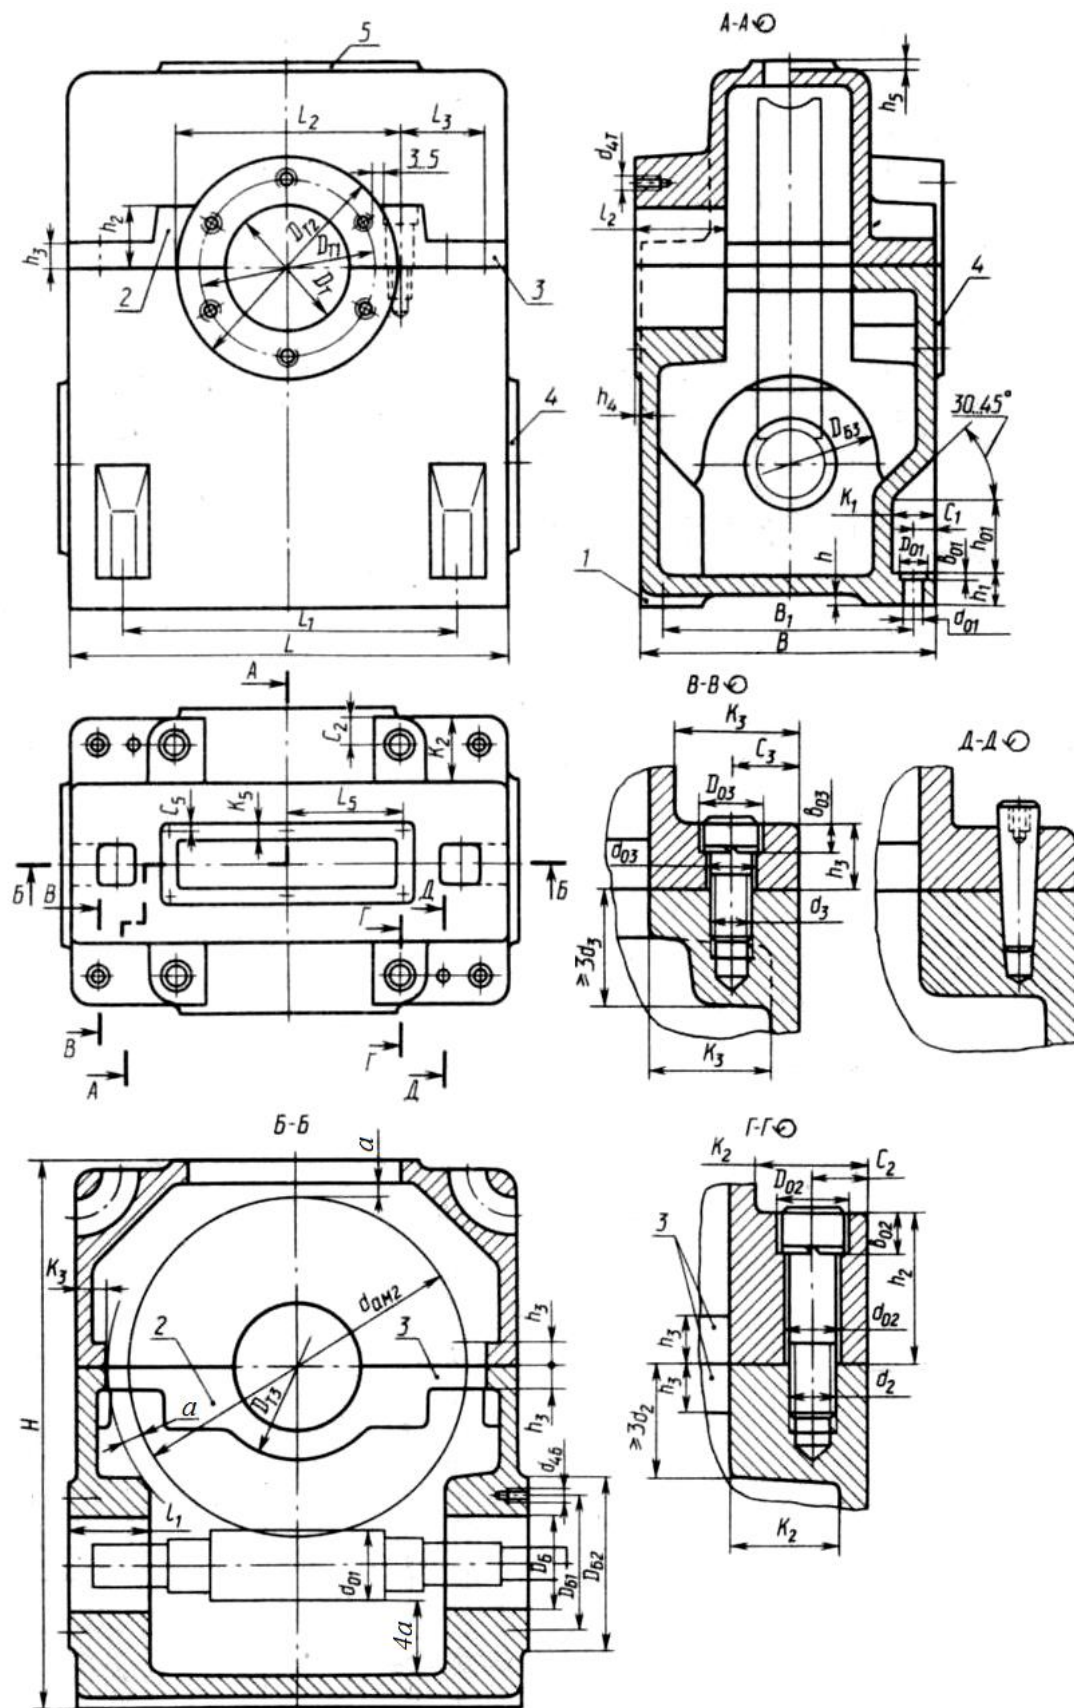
Разборный корпус одноступенчатого червячного редуктора с нижним червяком
